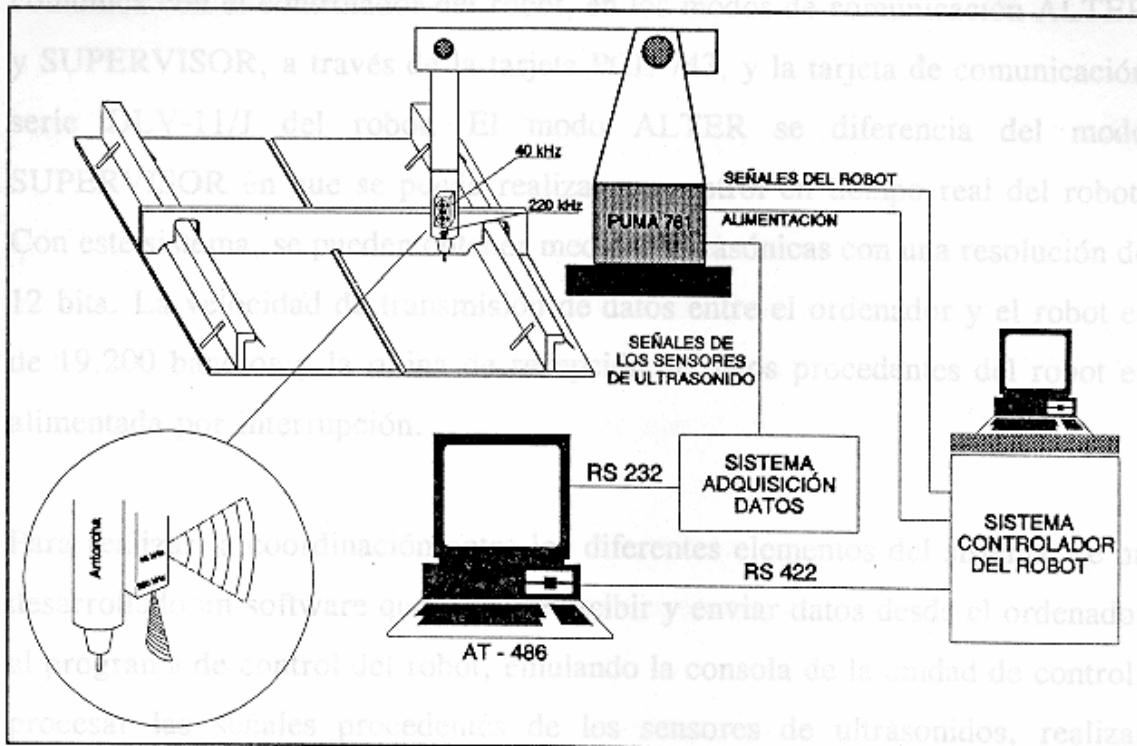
Componentes de um sistema de soldagem robotizada que utiliza sensores de ultra-som para busca das juntas a soldar, determina a distância às peças e realiza o seguimento do cordão a soldar [5].
